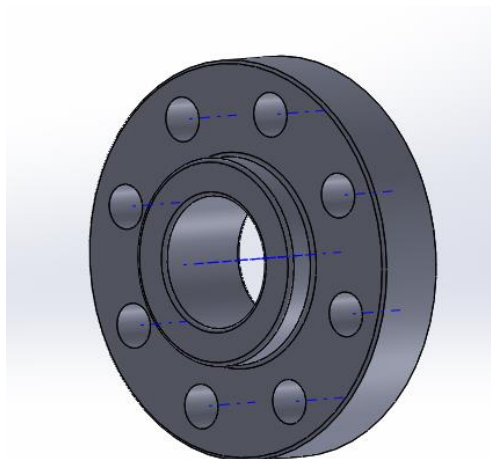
Perspectiva isométrica da junta flangeada (Autores)
